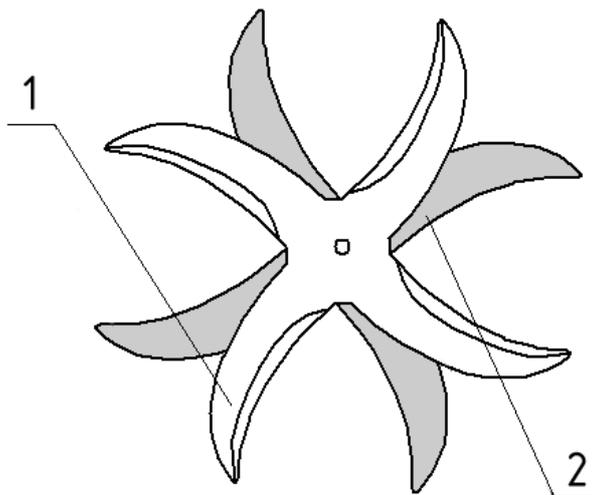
Схема многолезвийного режущего аппарата подпорного действия с двумя вращающимися роторами
